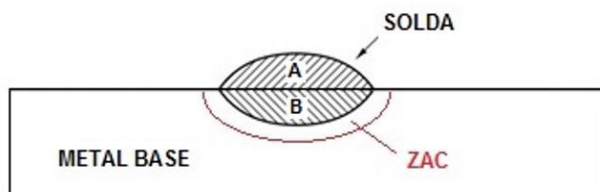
Perfil típico de cordão de solda. Adaptado de Singh et al. [8].
